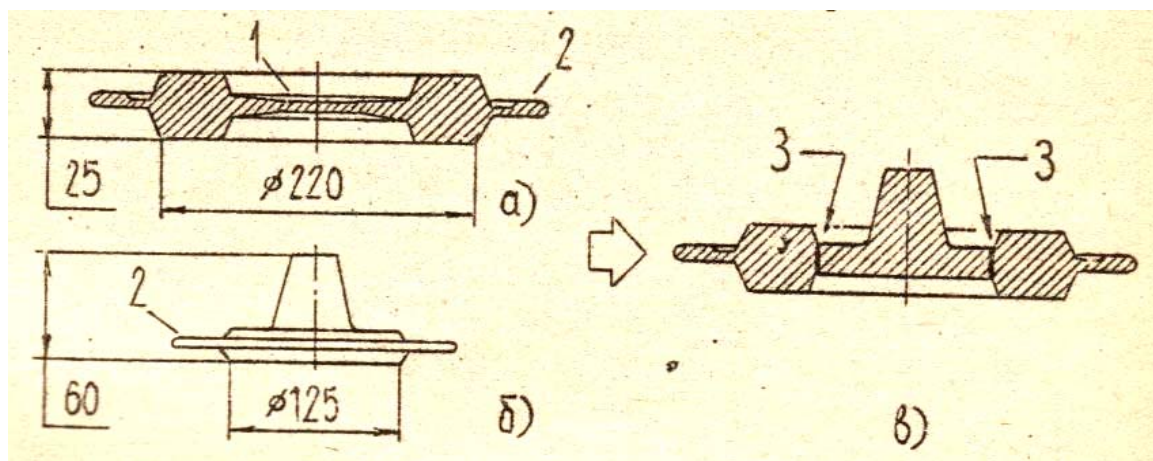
Изготовление поковок совмещенной штамповкой:
